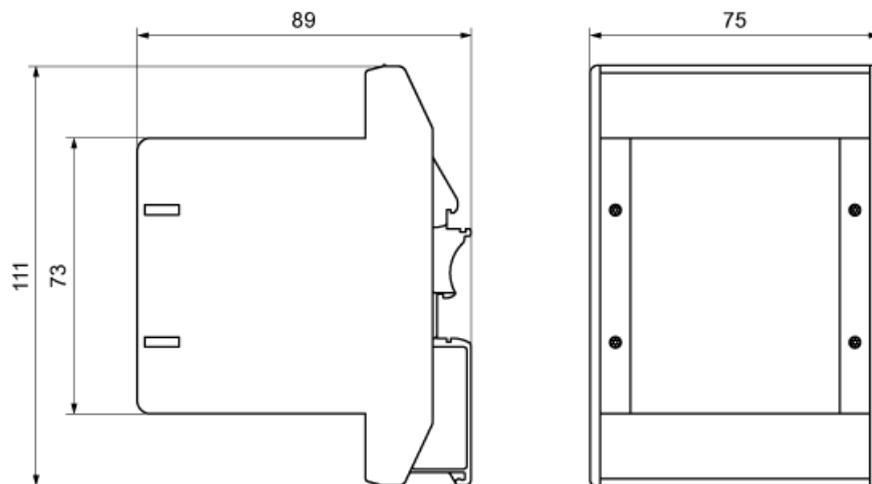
Maßbild Safe Brake Adapter (Angaben in mm)
